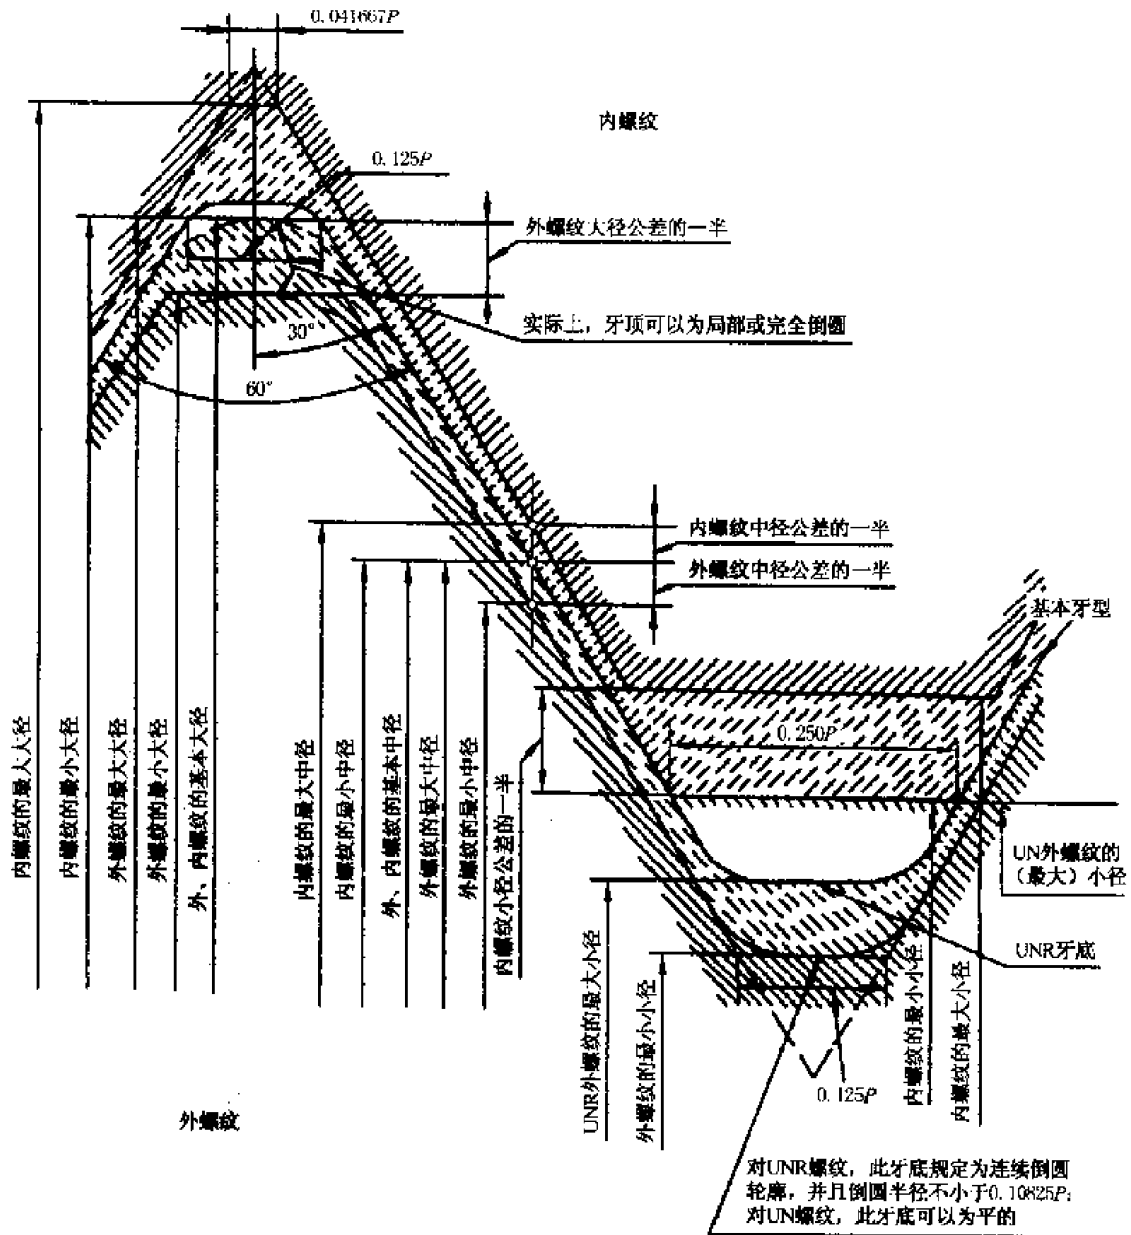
3A 和 3B 统一螺纹的公差带位置
